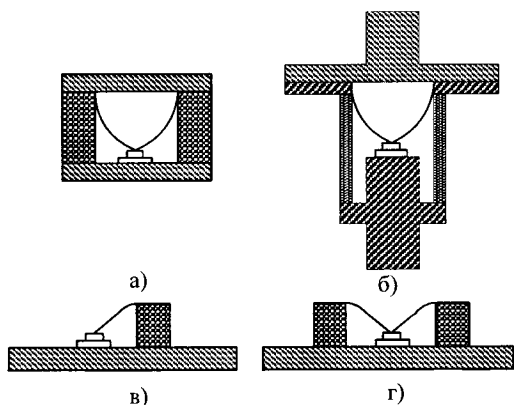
Конструкції р-і-п-діодів: а) кварцовий корпус; б) металокерамічний корпус; в) на штифтах з однією металізованою опорою; г) на штифтах з двома металізованими опорами
